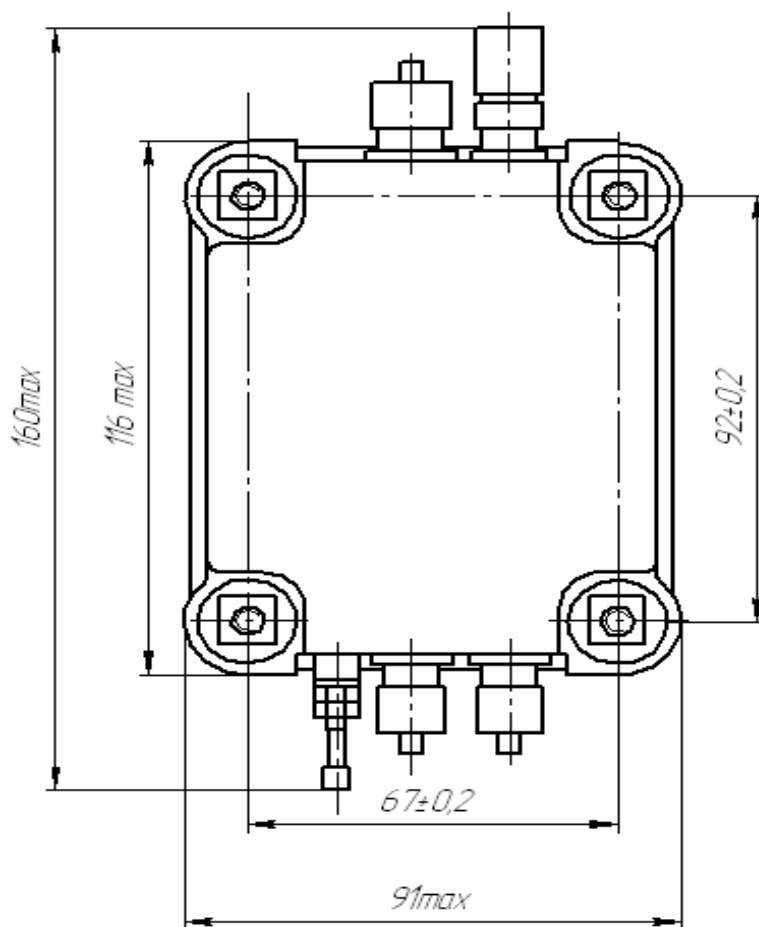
Габаритно-установочные размеры преобразователя Магнит-7Л
